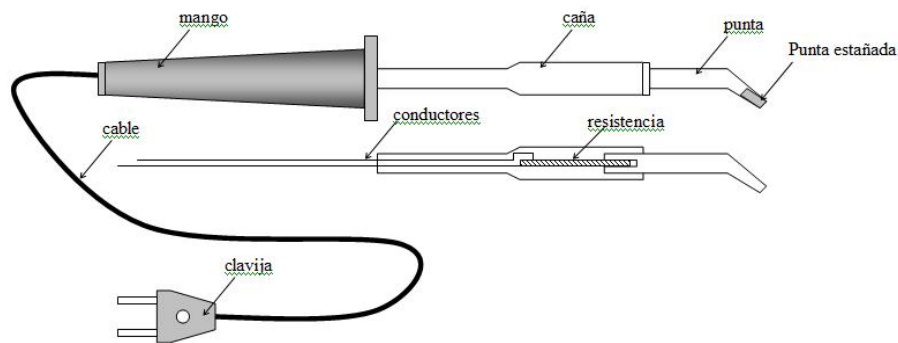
Despiece de soldador eléctrico. [H-43]
